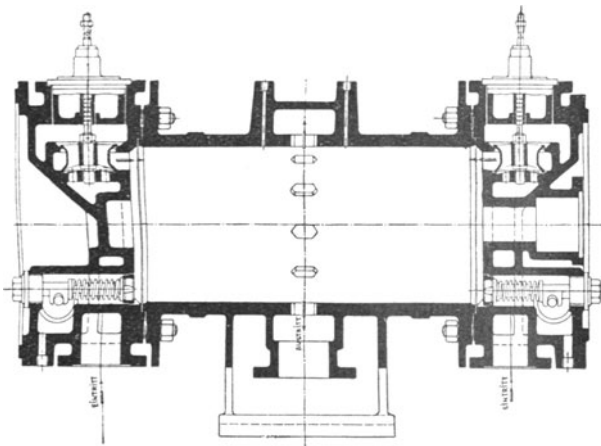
Gleichstromzylinder der Cottbusser Maschinenbauanstalt A.-G. mit Zuschaltventilen für Auspuffbetrieb.
